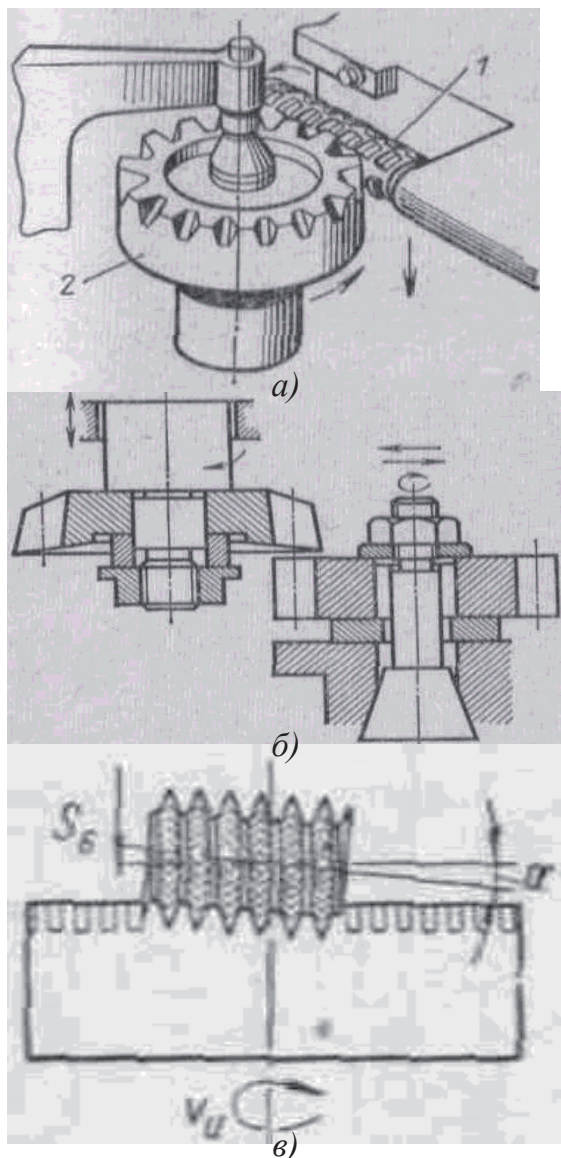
Нарезание зубчатых колес по методу обката: *a* – на зубофрезерных станках; *б* – на зубодолбежных станках, *в* – поворот оси червячной фрезы относительно заготовки
